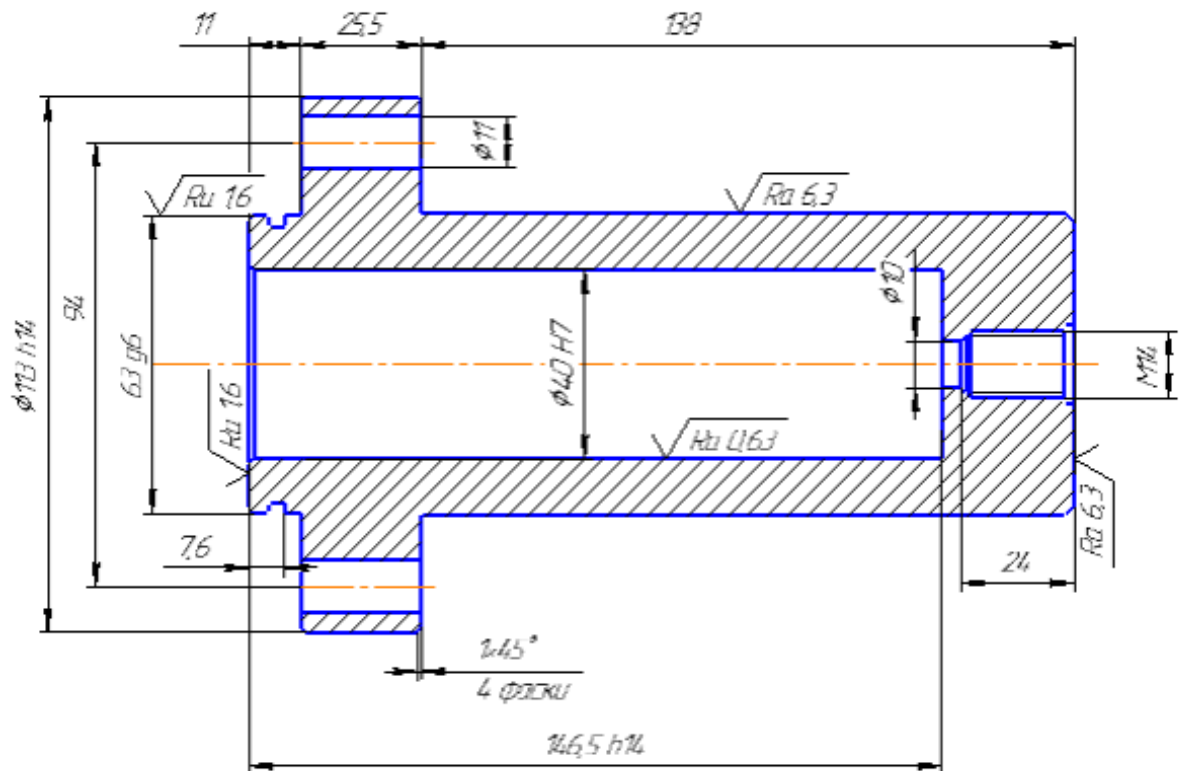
Креслення оброблюваної деталі з необхідними розмірами
